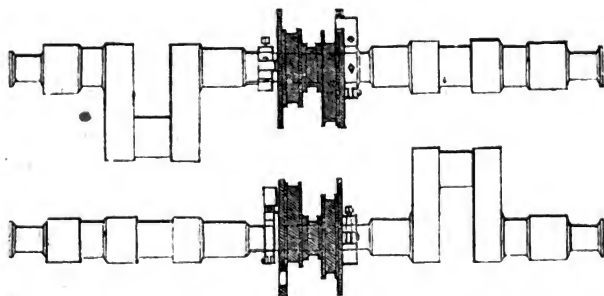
et 44. Arbres à manivelles, ou essieux coudés portant les roues motrices.
